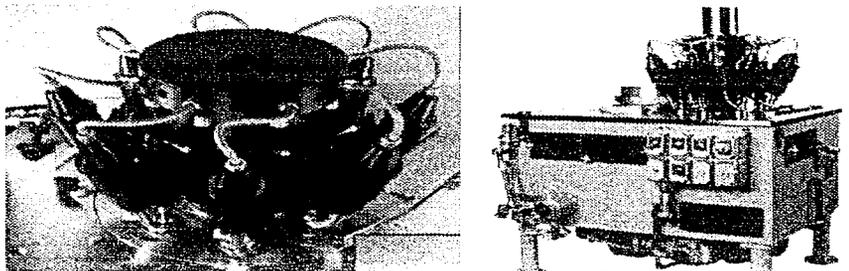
Engomadora rotatoria de ocho estaciones 8 III S, con pistola electrónica, cortesía de Preferred MACHINING Corporation
